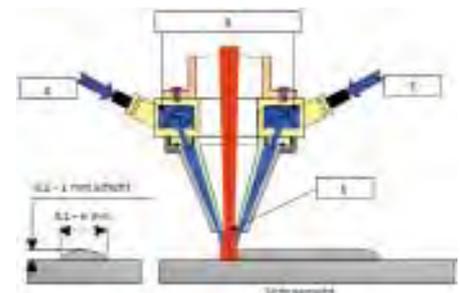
Grundprinzip des Laserauftragschweißens [2]
